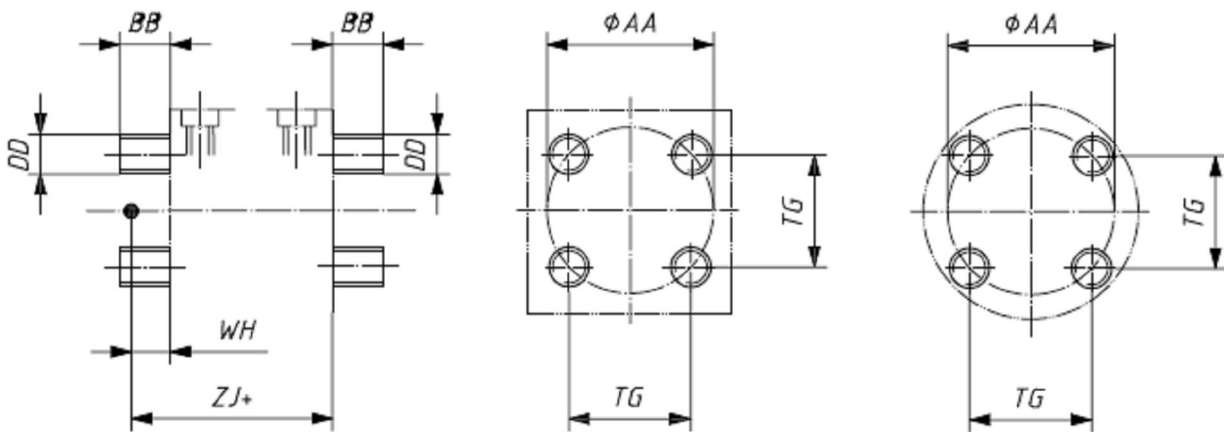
MDT4: Trục xoay trung gian cố định hoặc di động (bị bao) – Hai cần pit tông
